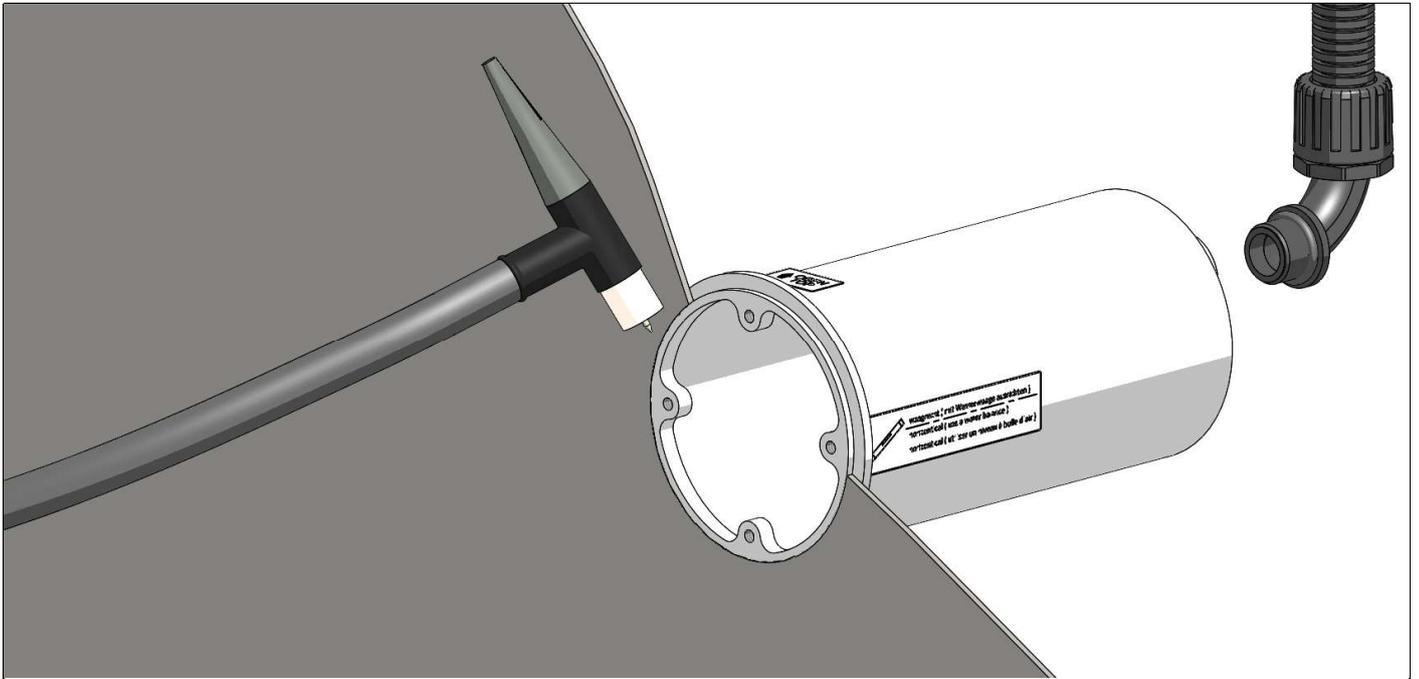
Boîtier à sceller bassin en inox – soudage à fleur avec le bassin (procéder ensuite au montage étanche du système de protection des câbles)
